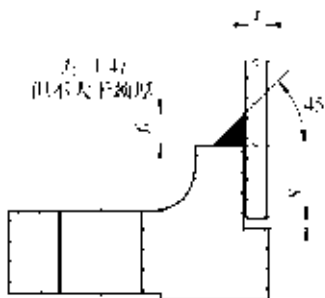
承插焊法兰与钢管连接的焊接坡口形式及尺寸
